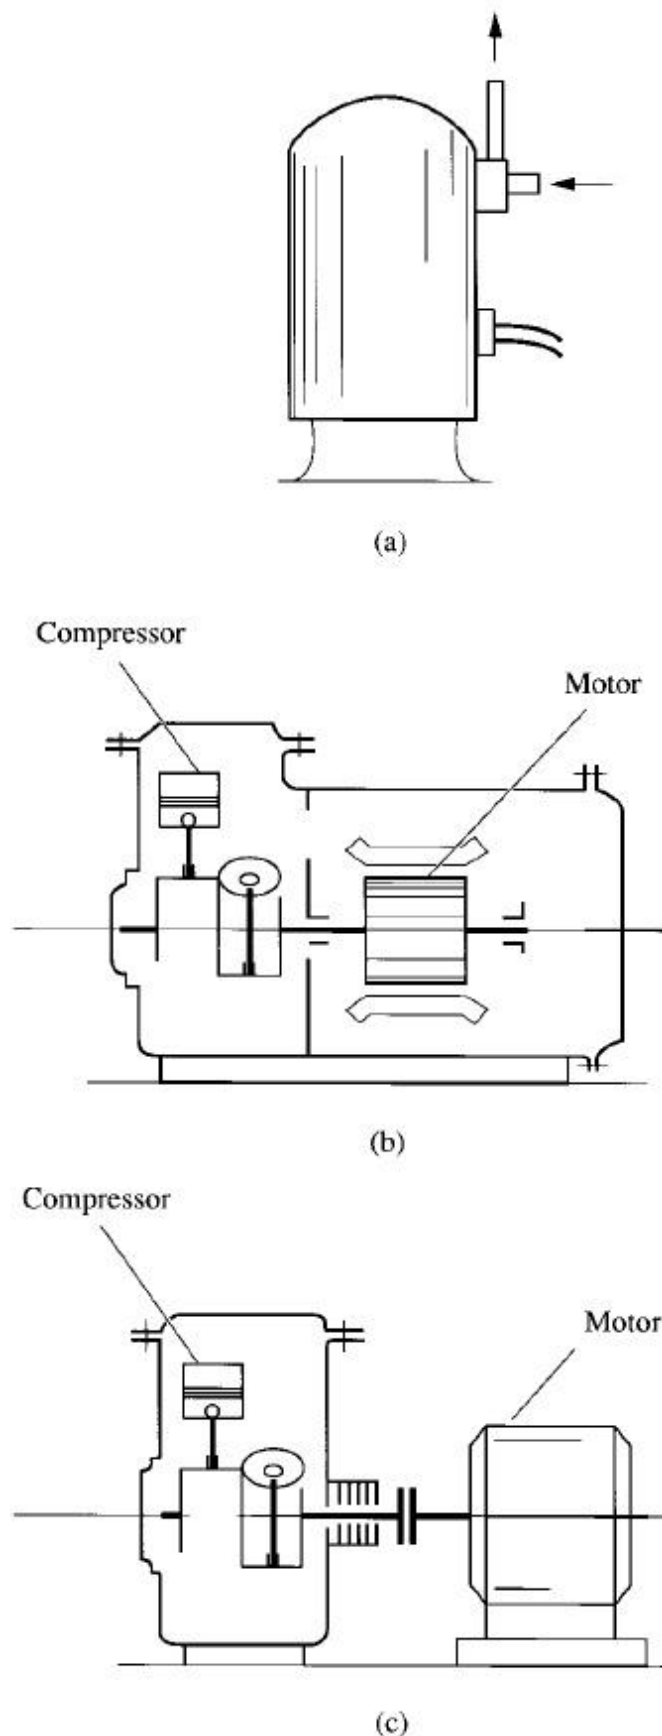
Compressor hermético 3a, Compressor Semi-hermético 3b, Compressor aberto 3c [12]
